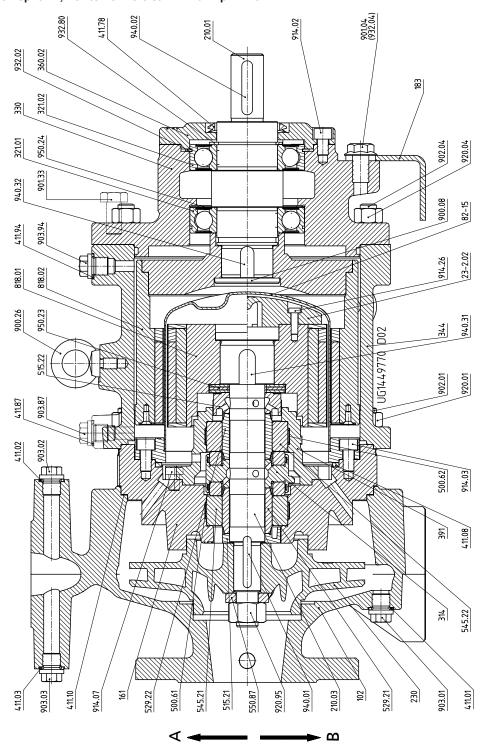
Сборочный чертеж, исполнение с зажимной крышкой без переходника
